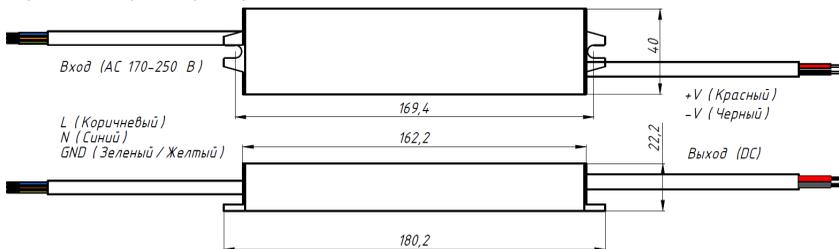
Габаритные размеры блока питания Geniled GL-12V75WM67.
